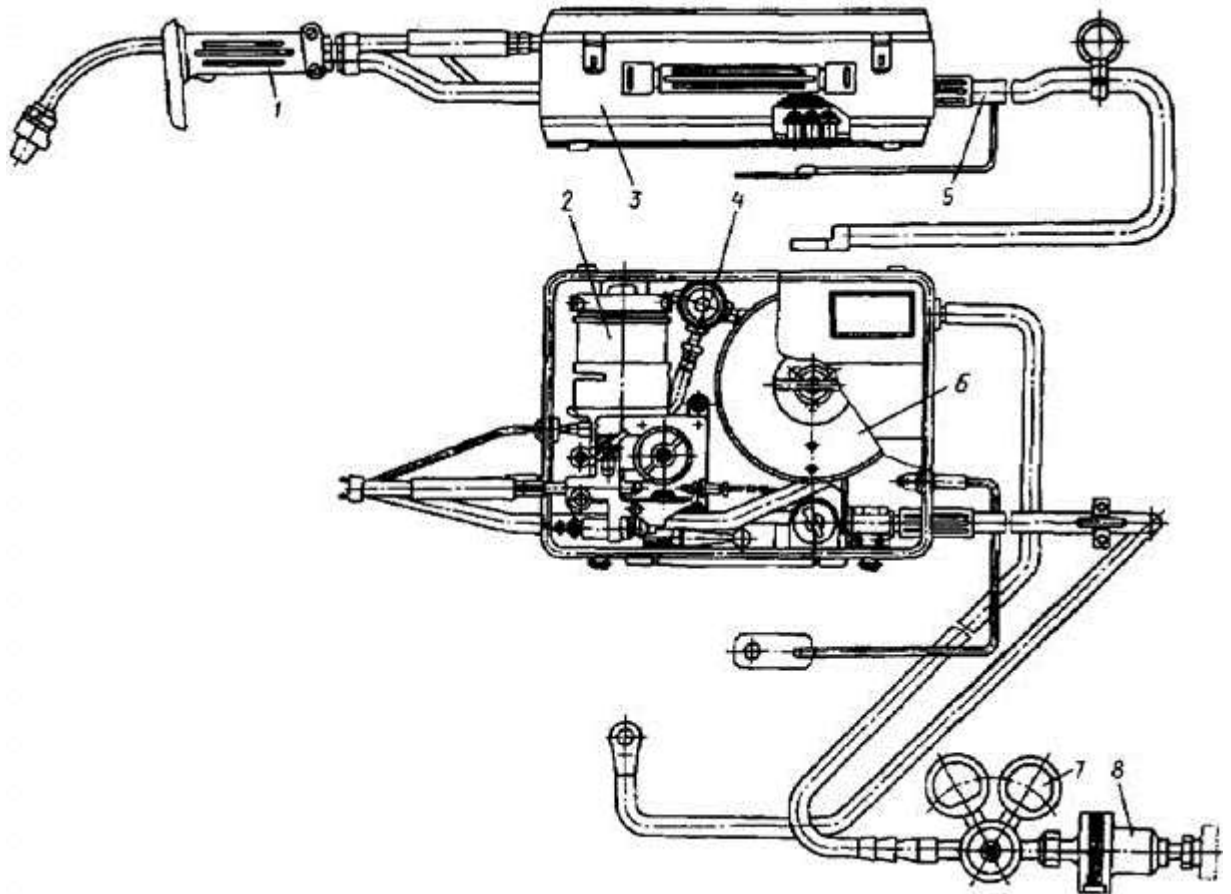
Зварювальний напівавтомат А-1230М:
